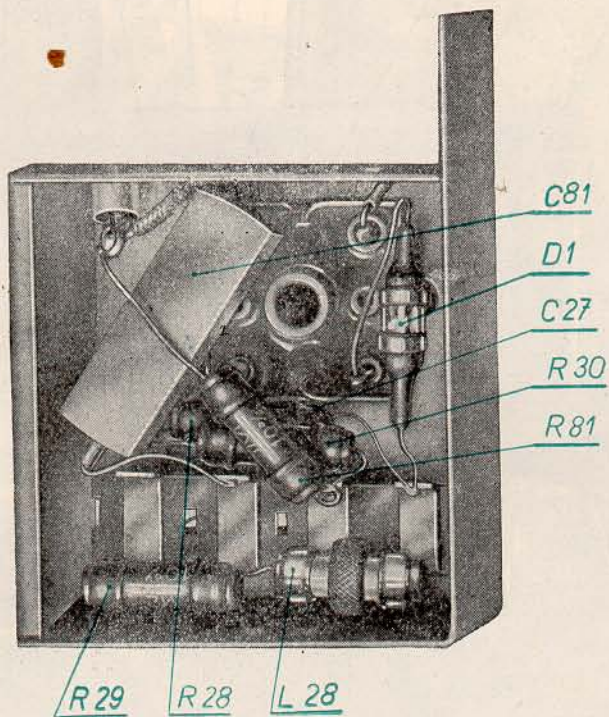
Rozmiestnenie dôležitých dielov pod chassis
